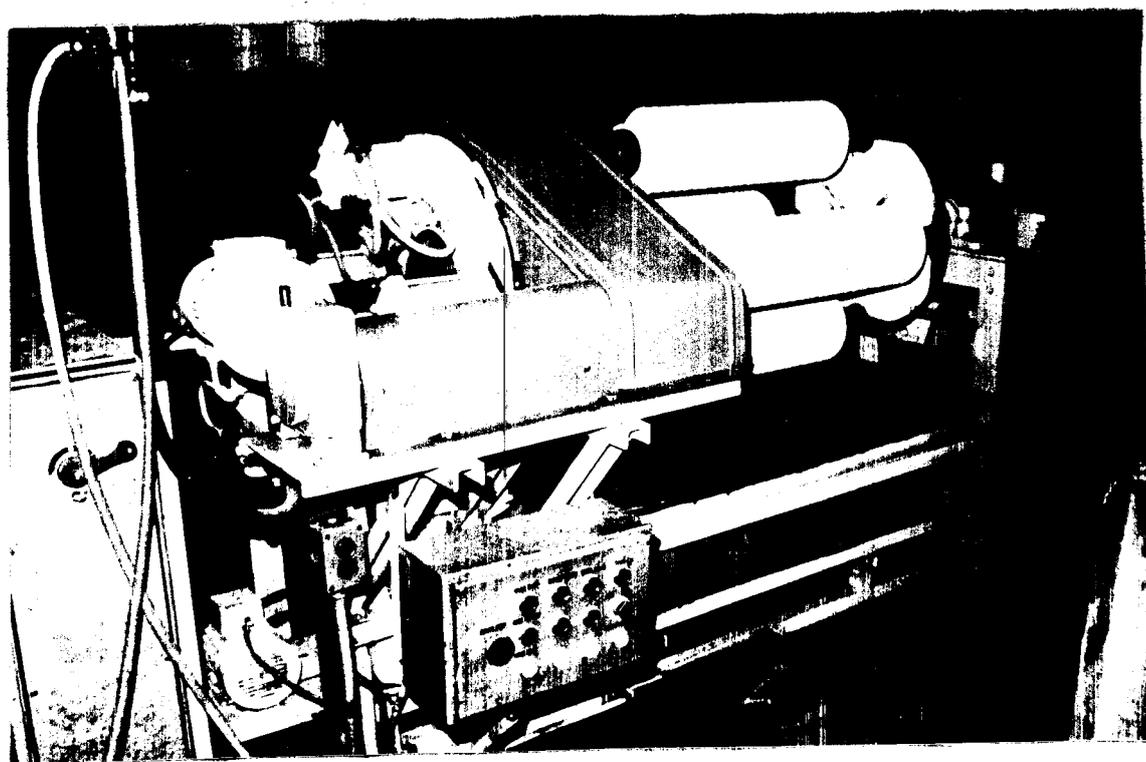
Glazovací stroj pro izolátory typu "Spirelec"
